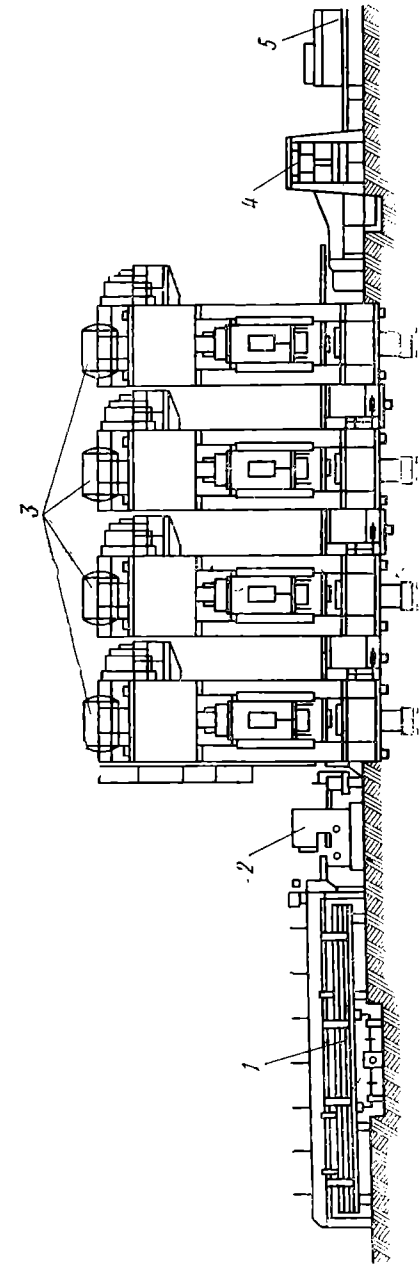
Автоматическая линия для штамповки фланцевых дисков
